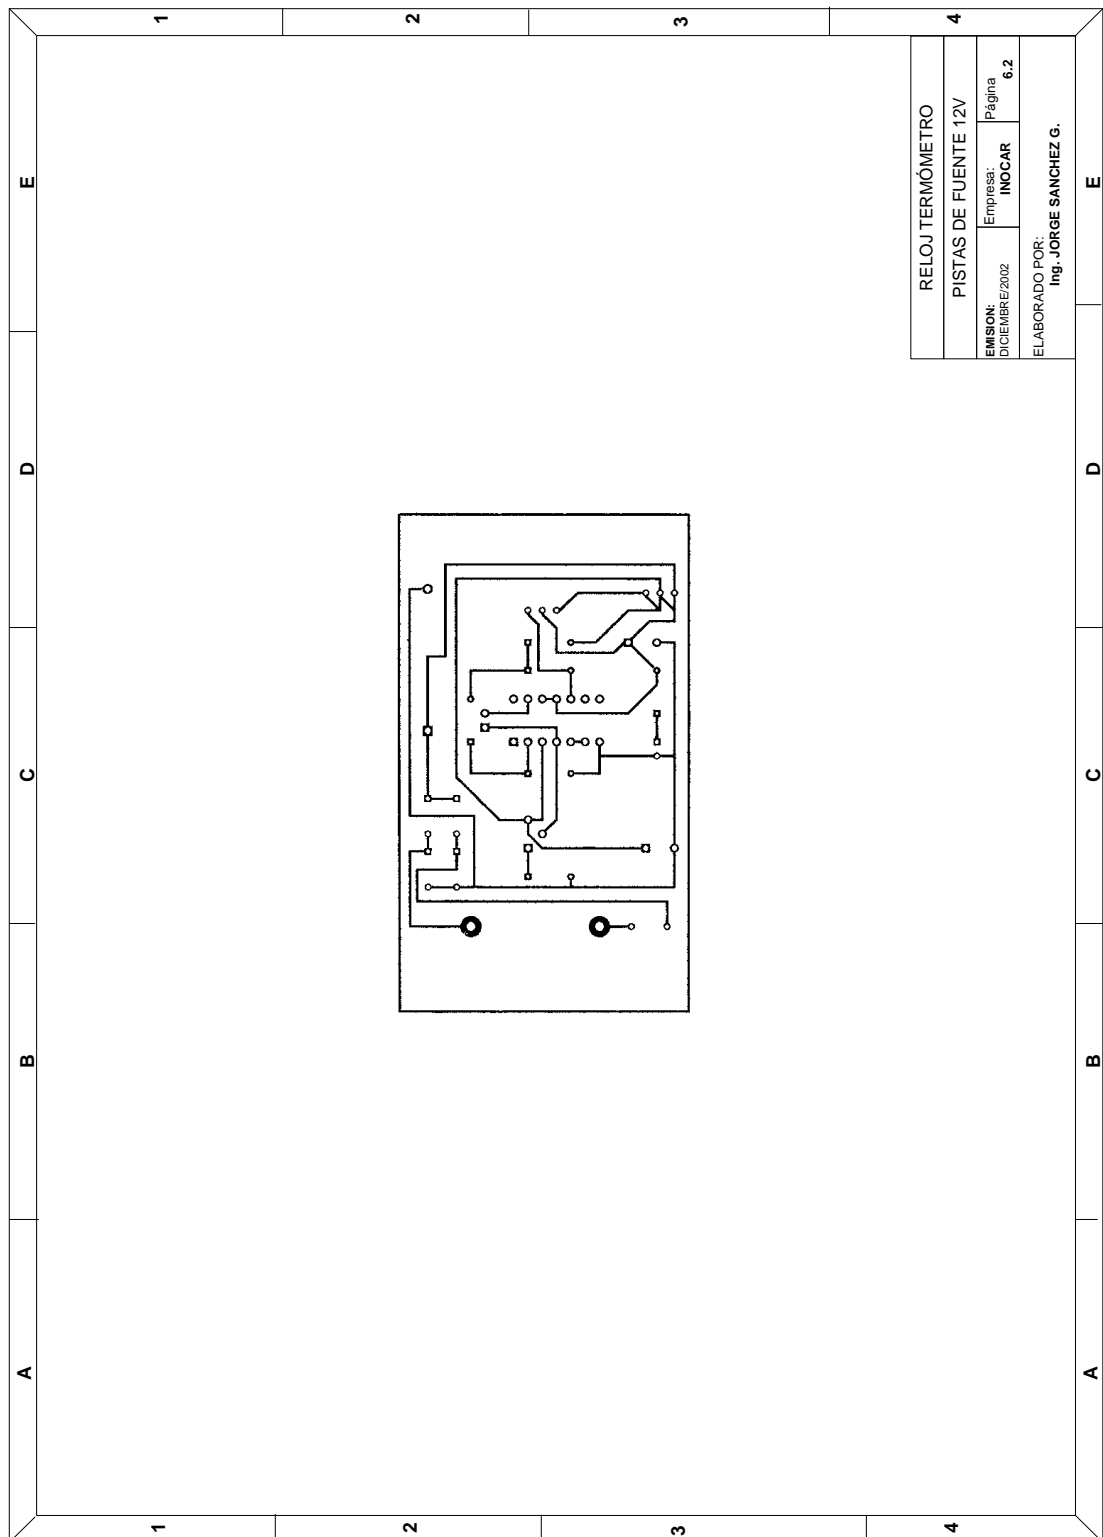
Tarjeta de fuente 12VDC(Diagrama de pistas lado de soldadura)
